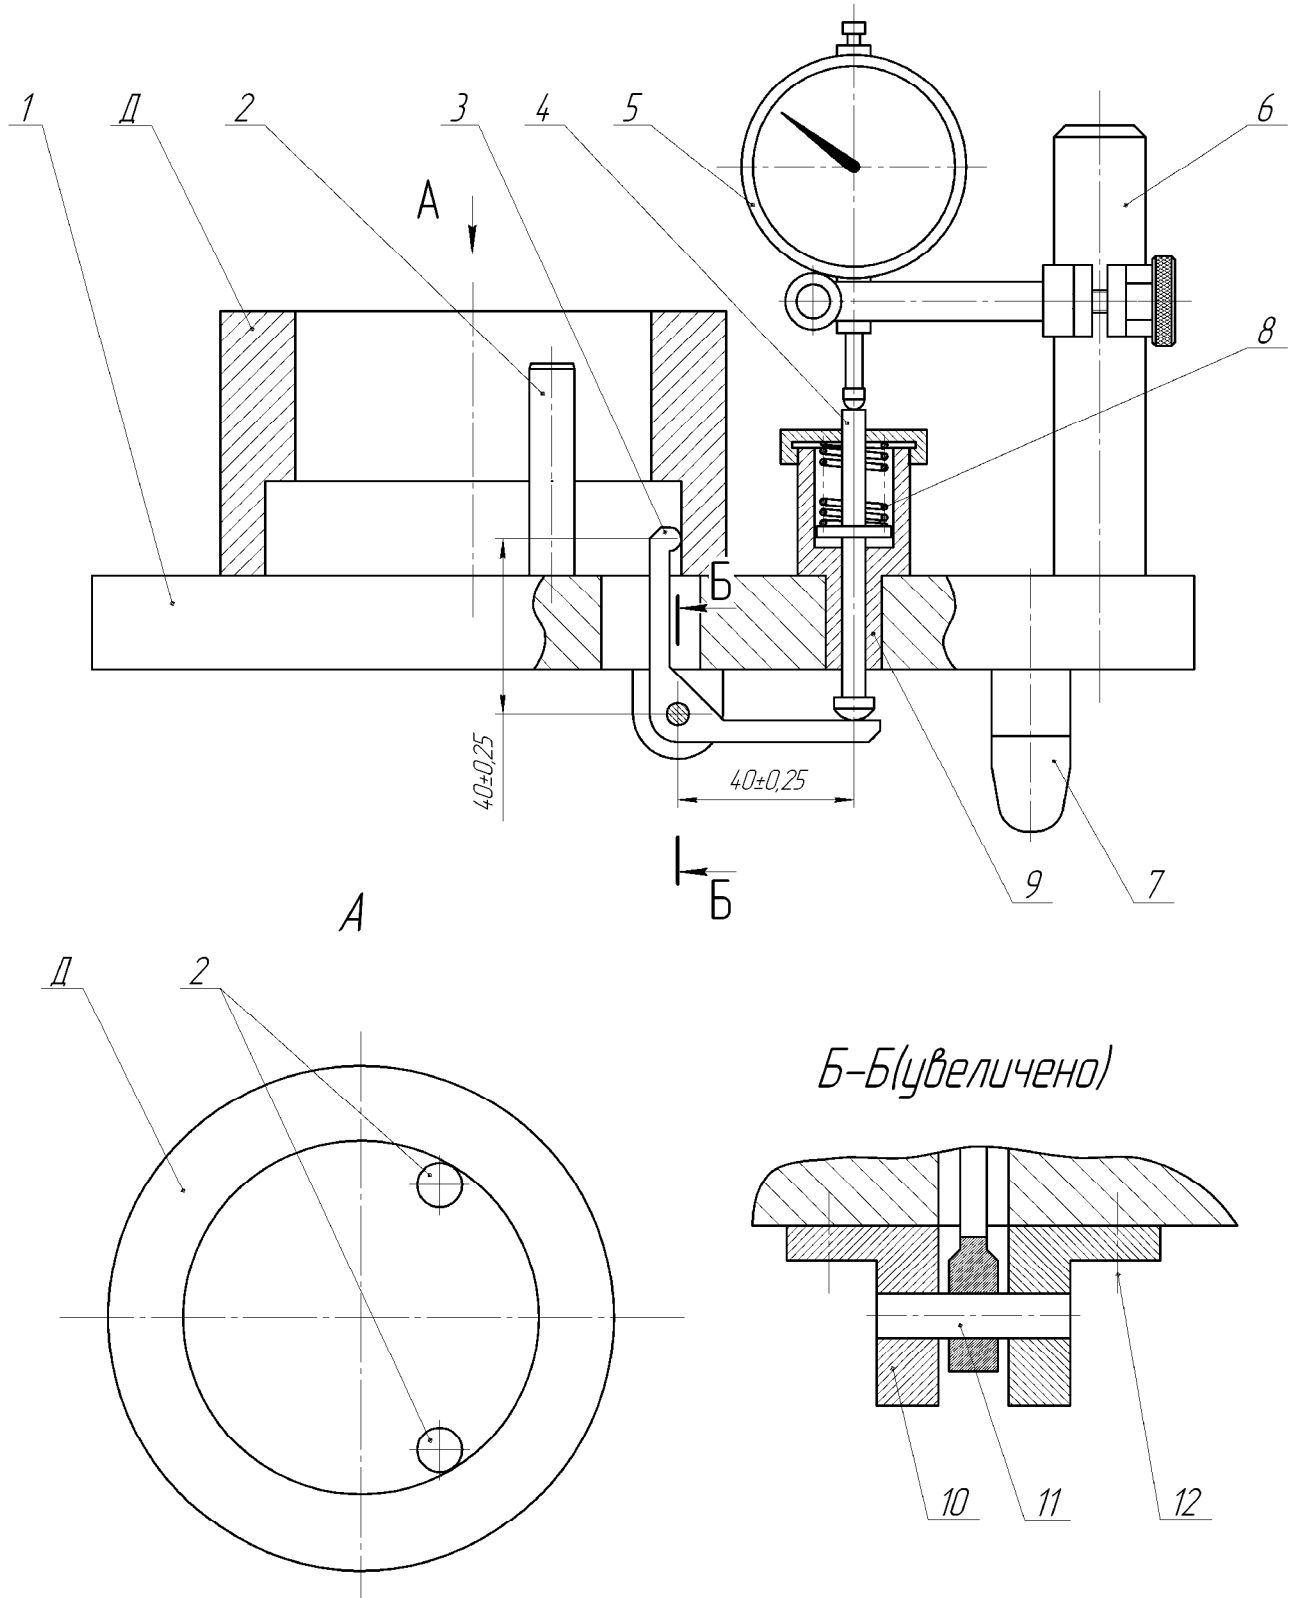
Приспособление для контроля радиального биения внутренних цилиндрических поверхностей детали:
